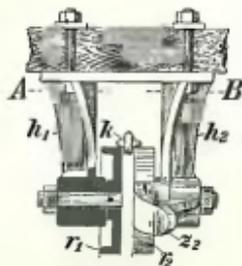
Kettenträgerrolle für Gabelmitnehmer.
